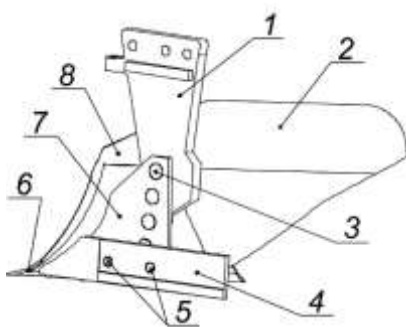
Корпус: 1 – стойка; 2 – крыло отвала; 3 – болт; 4 – доска полевая; 5 – болт с шайбой и гайкой; 6 – лемех; 7 – башмак; 8 – грудь отвала
